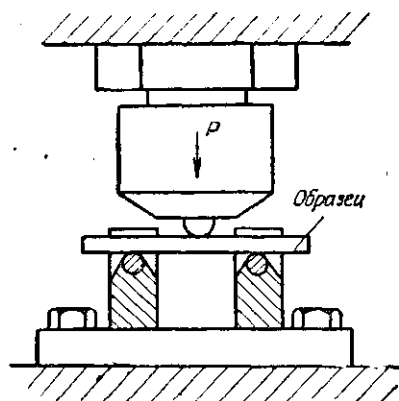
Приспособление для испытания на изгиб на прессе Бригеля (Скэнлан и Зеелиг)
